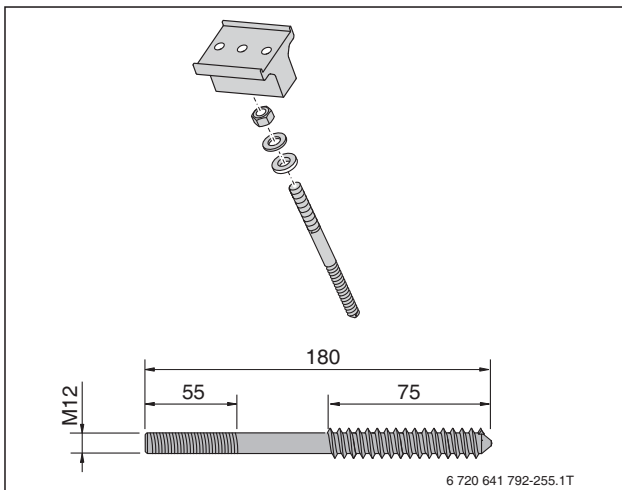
Stockschraube für die Dachanbindung Wellplatten-, Blechdach (Maße in mm)
